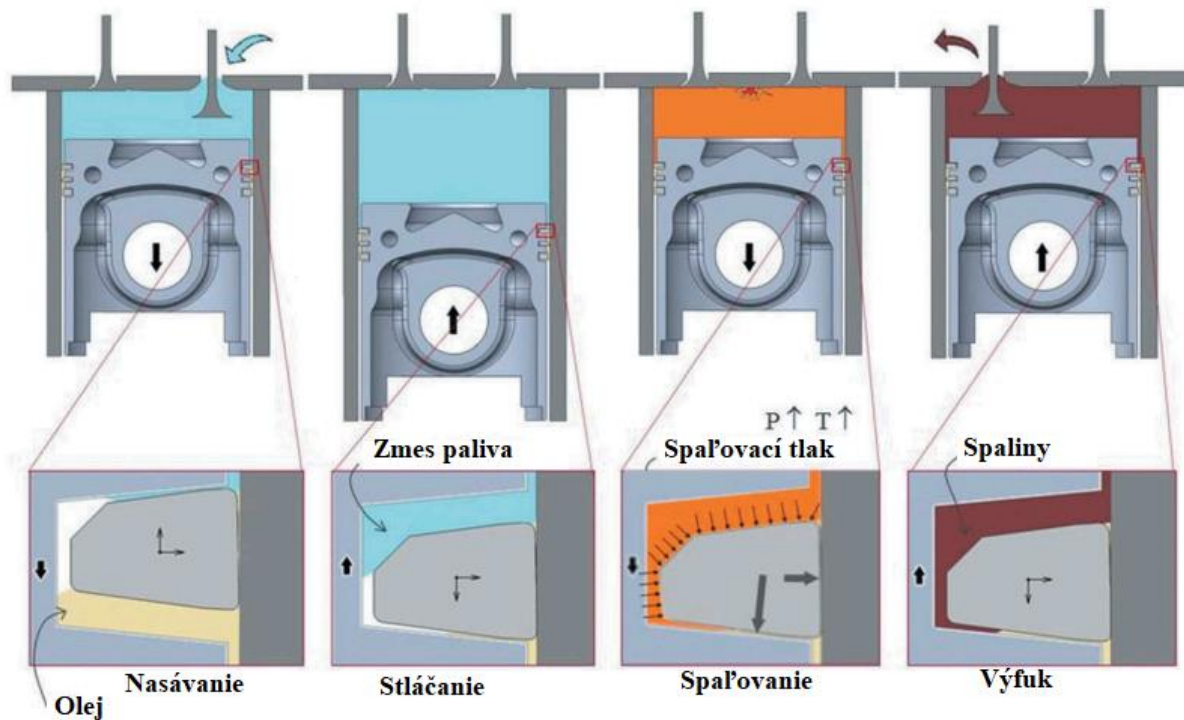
Rauscher, J., Spalovací motory. VUT FSI Brno, 2005.
